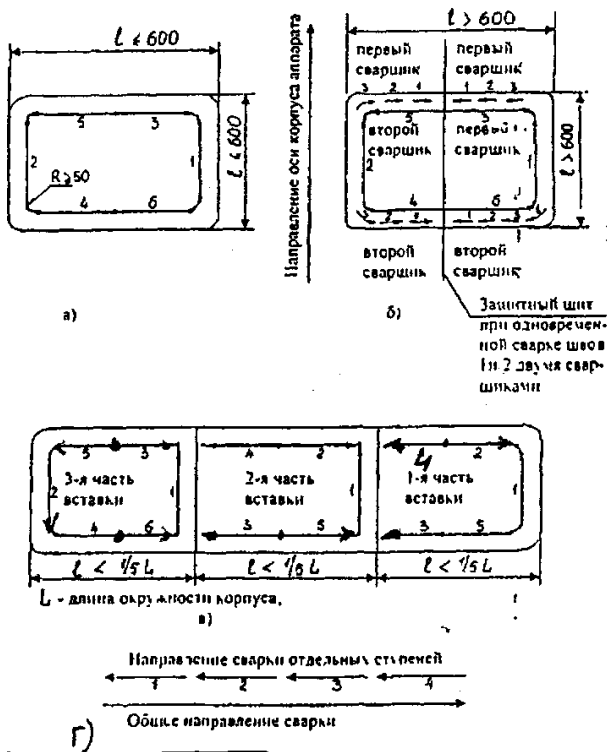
Последовательность выполнения каждого слоя сварного шва: а) сварка каждого слоя вставки длиной по окружности корпуса до 600 мм; б) сварка каждого слоя вставки длиной по окружности корпуса до 600 мм обратноступенчатым способом; в) сварка каждого слоя вставки длиной по окружности корпуса более $1/5$ периметра (вся вставка разделена на 3 части, ввариваемые последовательно); г) принципы обратноступенчатого способа сварки
